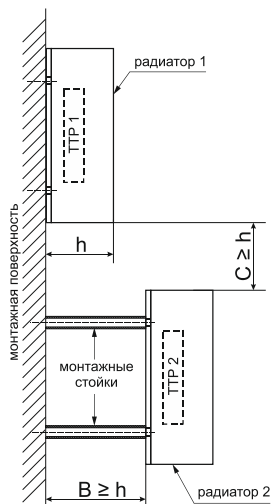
схема размещения ТТР при монтаже друг над другом
